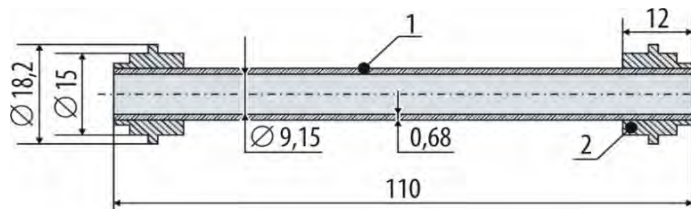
Эскиз патрубка, используемого для изготовления трубчатого образца для испытаний оболочки облучённого твэла на ползучесть: 1 — трубчатый образец; 2 — втулка
